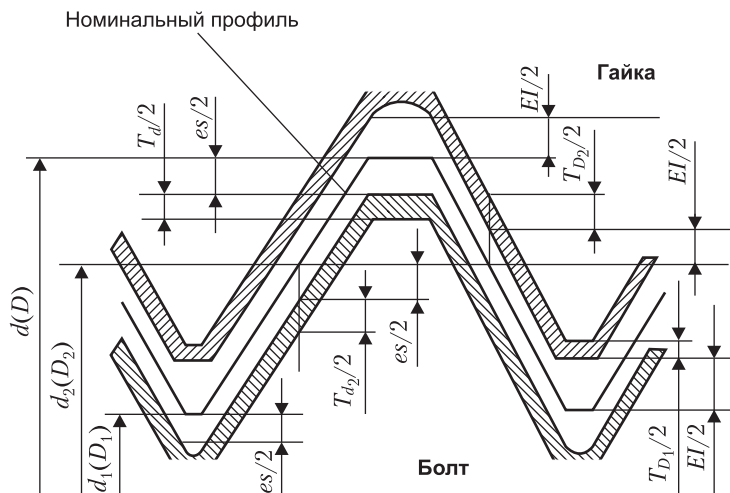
Расположение полей допусков метрической резьбы при посадке с зазором. Установлены ряды основных отклонений: для болтов h, g, f, e, d ; для гаек H, G, E, F
